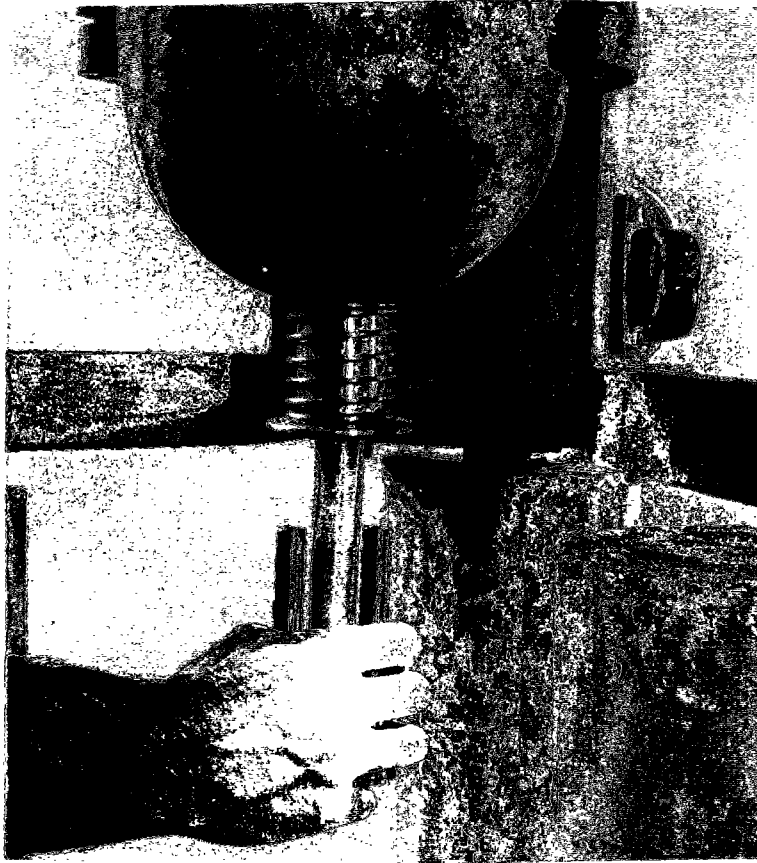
vue de la cuve équipée du clapet, et remplissage d'un moule.
